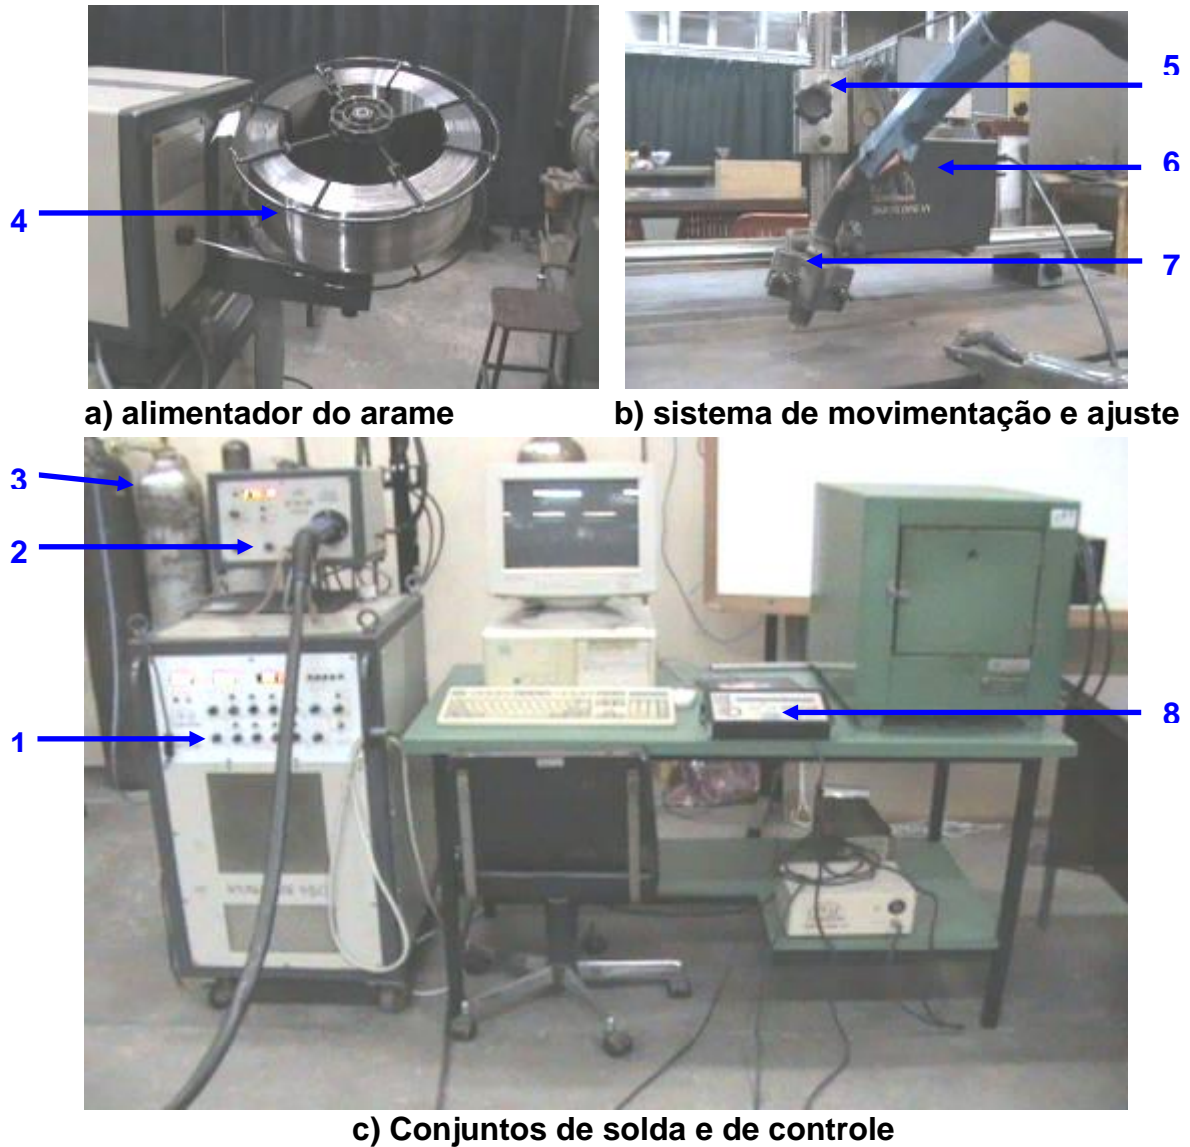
Equipamentos utilizados para soldagem dos experimentos.
